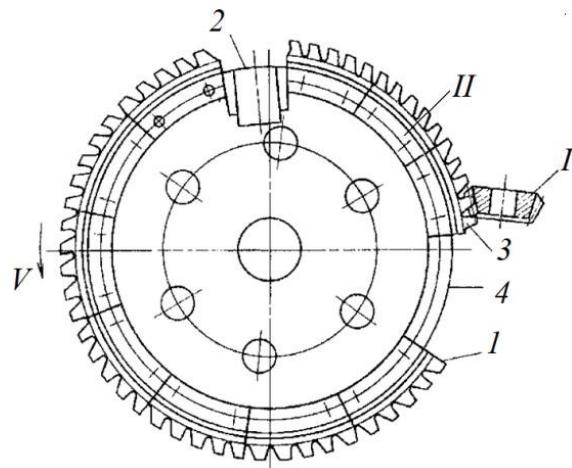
Схема роботи кругової протяжки [33]
